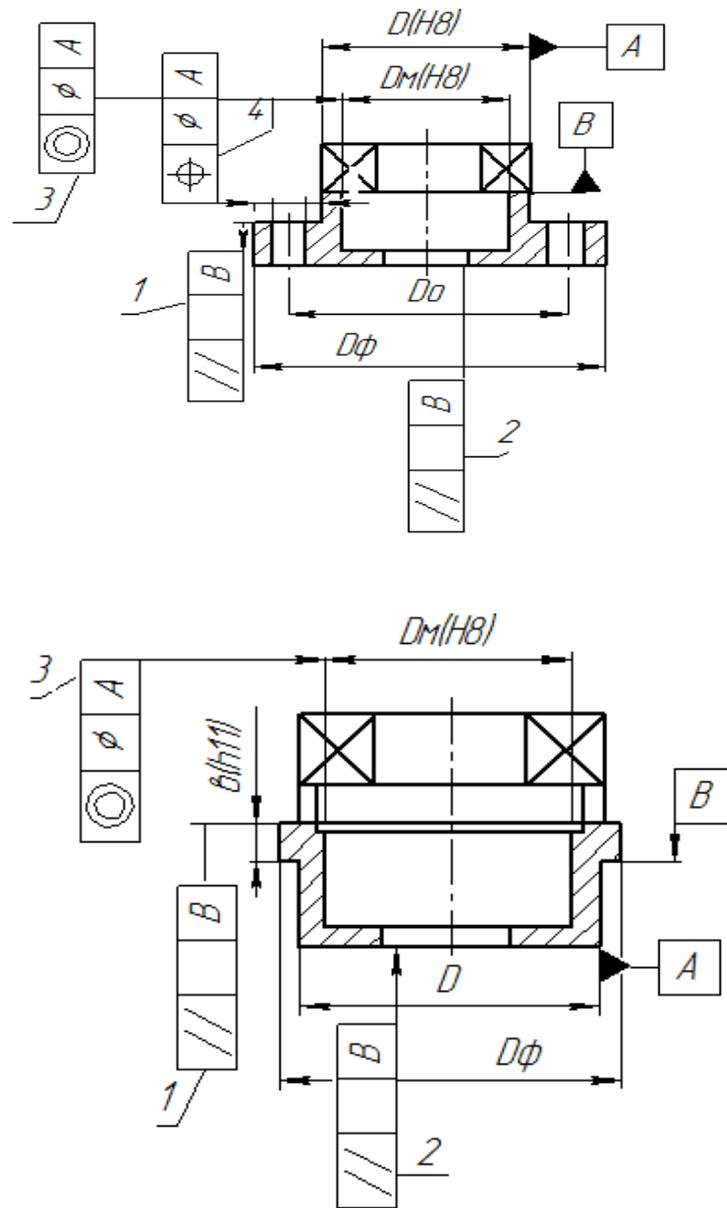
Позиции допусков и расположения поверхностей
